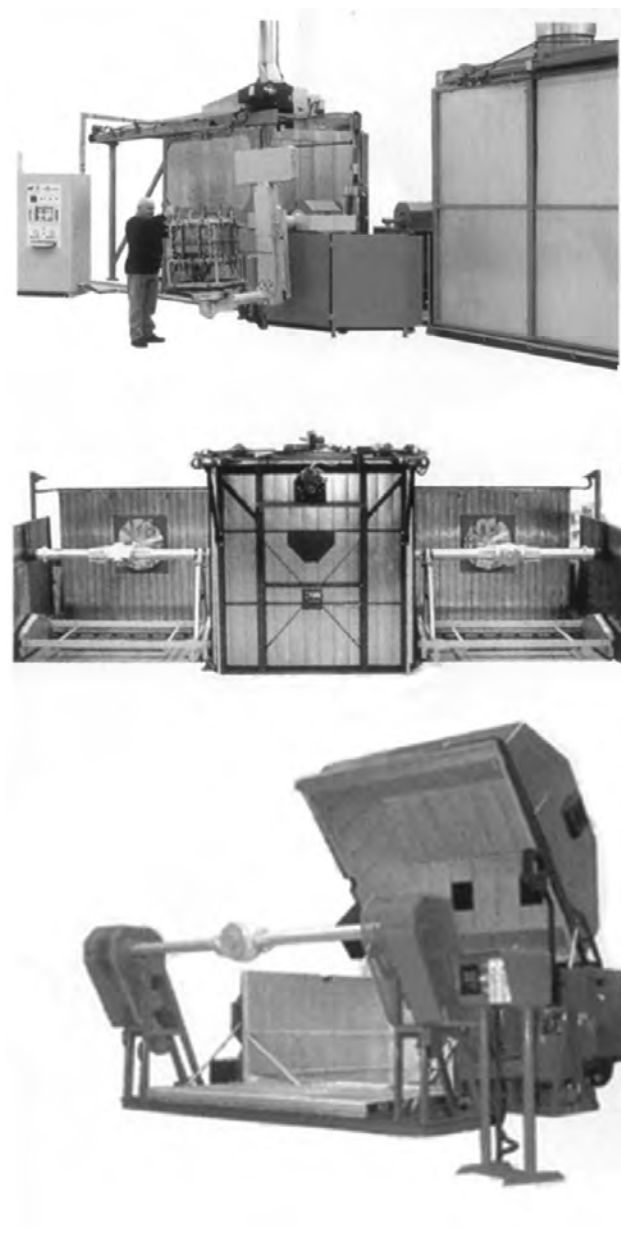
Maquinarias utilizadas por el rotomoldeo (Ferry Industries, Inc.)
